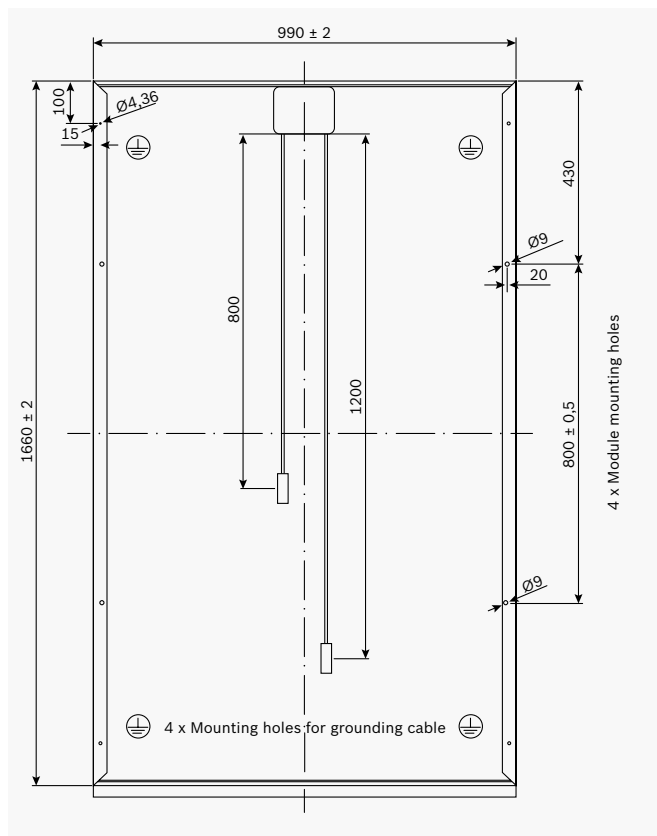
lado posterior do c-Si M 60 e M 60 S, P 60, fabricante 14, 17 e 23
